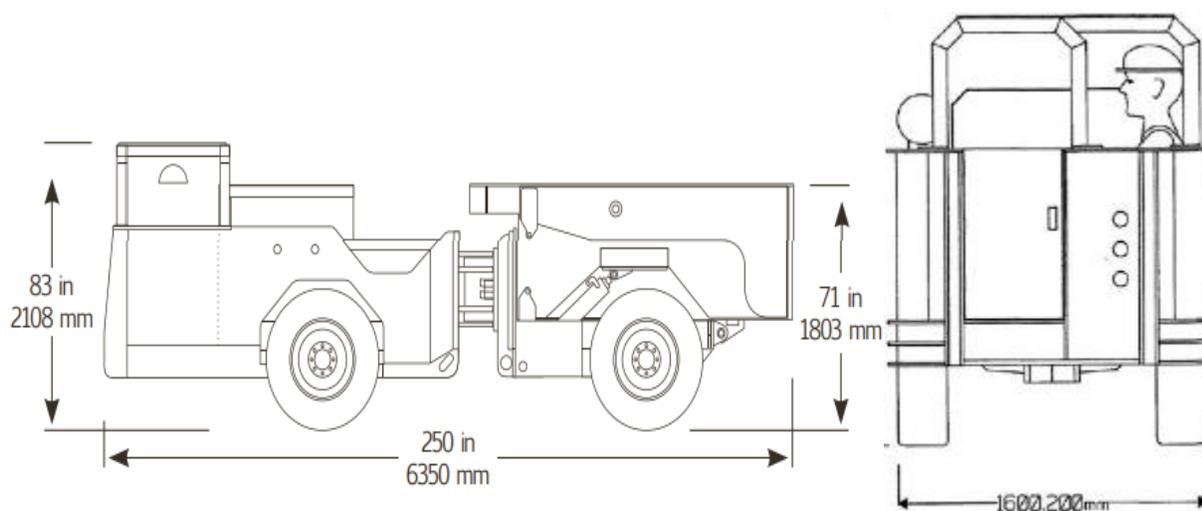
Dimensiones volqueta YMC 470T7. Fuente. YOUNGS MACHINE COMPANY
